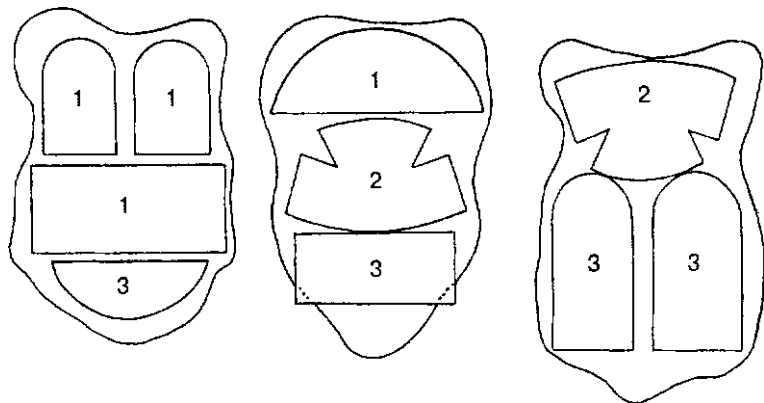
Схема раскроя трех шкурок кролика на детали цельно меховой шапки-ушанки:
